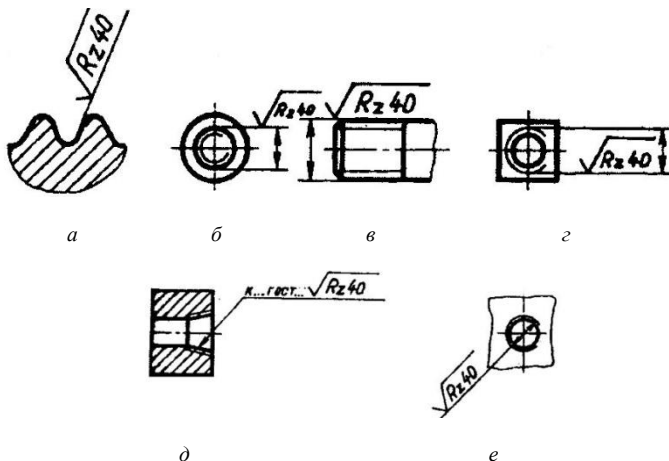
Простановка шероховатости для поверхностей с резьбой:
